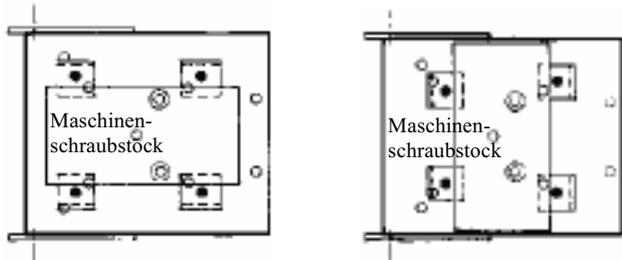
Befestigungspunkte für den Maschinschraubstock
